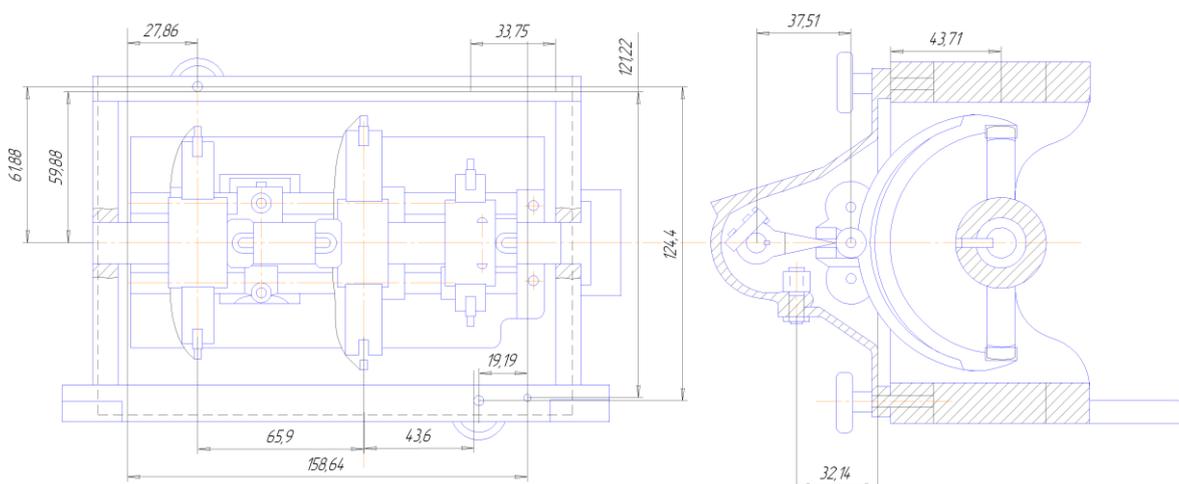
Контрольное приспособление для сборки и проверки правильности сборки крышки картера коробки передач
